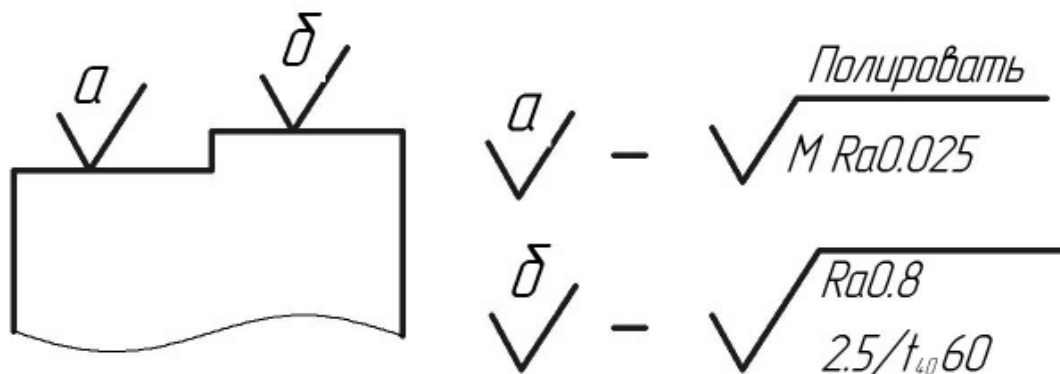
Пример упрощенного обозначения шероховатости поверхностей
